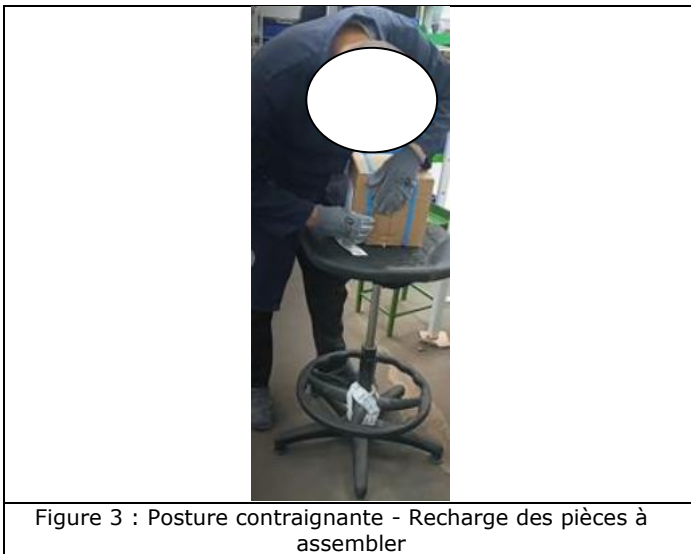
Posture contraignante - Recharge des pièces à assembler
